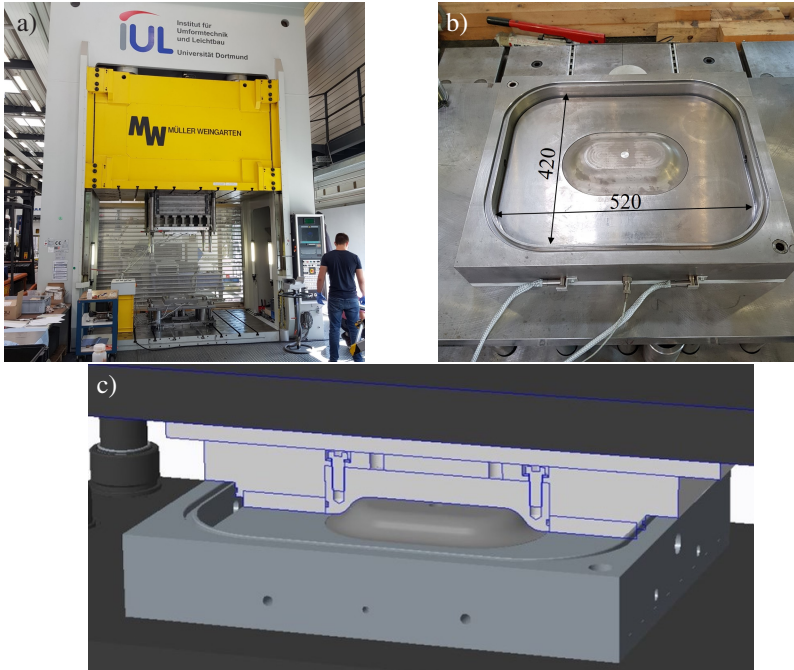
a) Presse des IUL Dortmund für die Herstellung der 3D-Bauteile; b) Werkzeug zur Herstellung von tiefgezogenen, hybriden FMEL-Bauteilen; c) Schnittansicht des CAD-Modells des Werkzeugs für die 3D-Bauteile.
